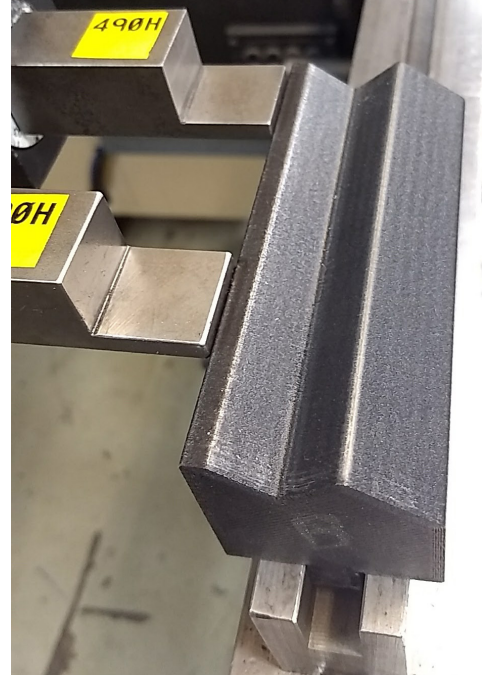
Gedrucktes Werkzeug in einer Abkantpresse
